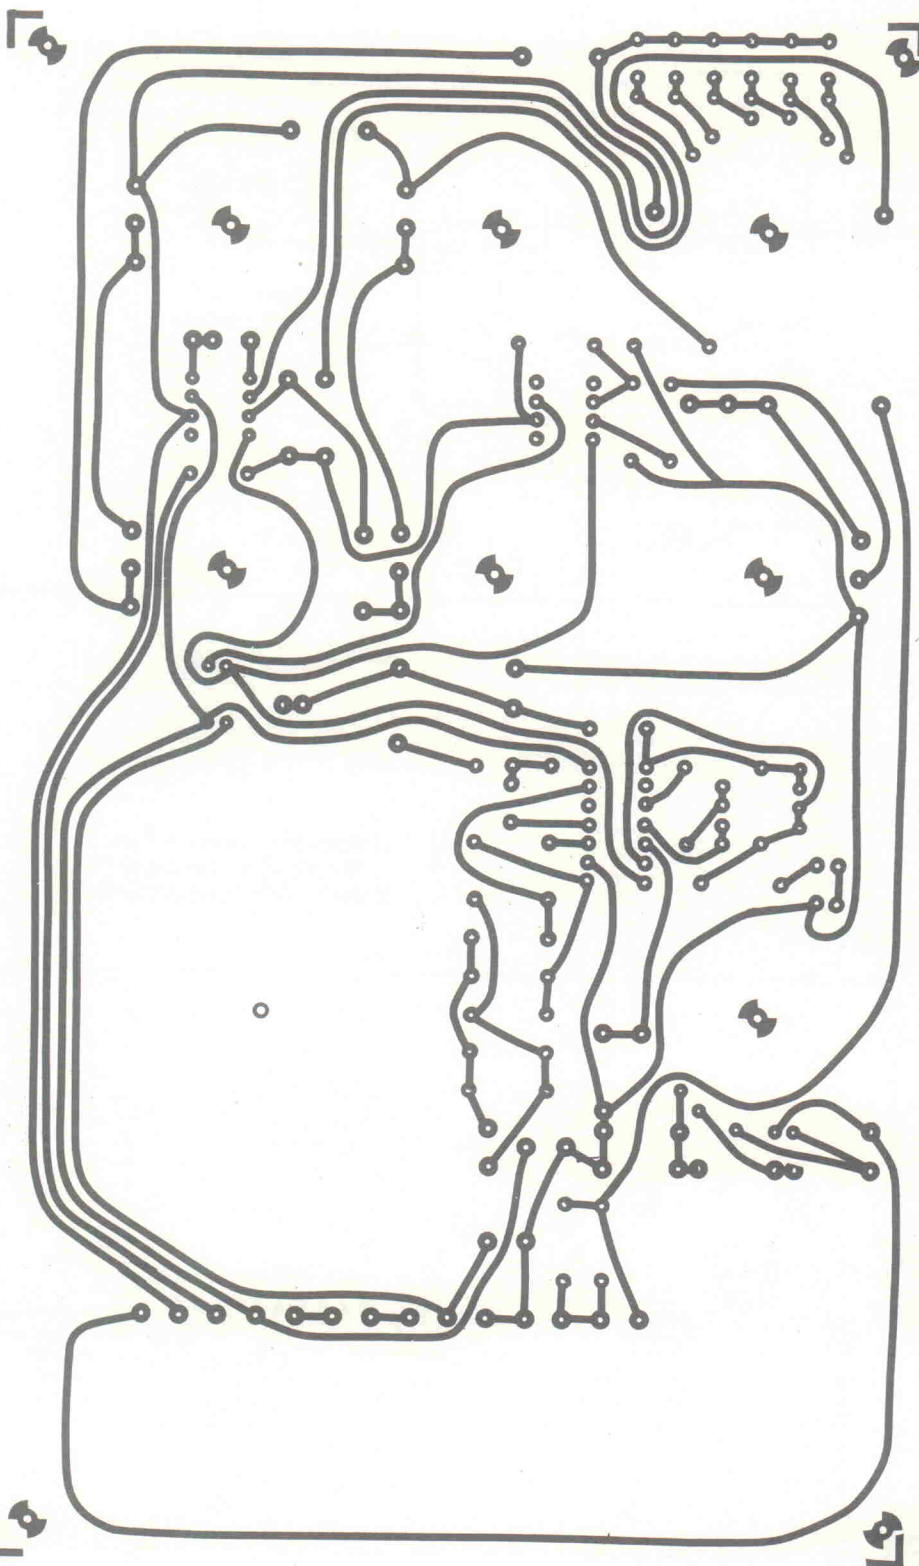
Das Platinen-Layout für das Klirrfaktor-Meßgerät
